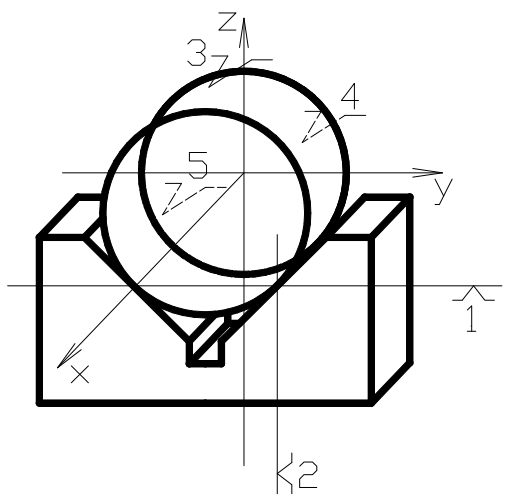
Базування по короткій зовнішній поверхні обертання
